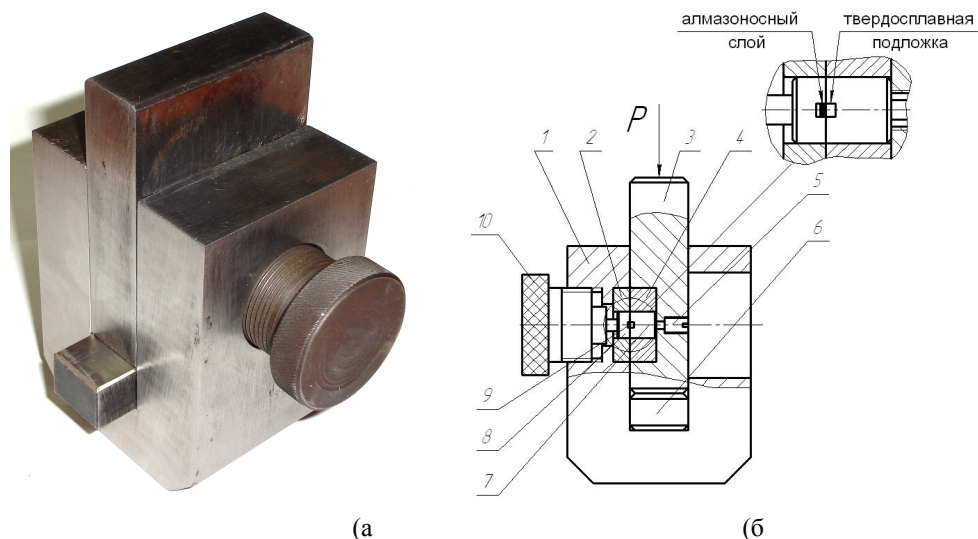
Приспособление для испытаний образцов на срез: а – общий вид, б – схематическое изображение
